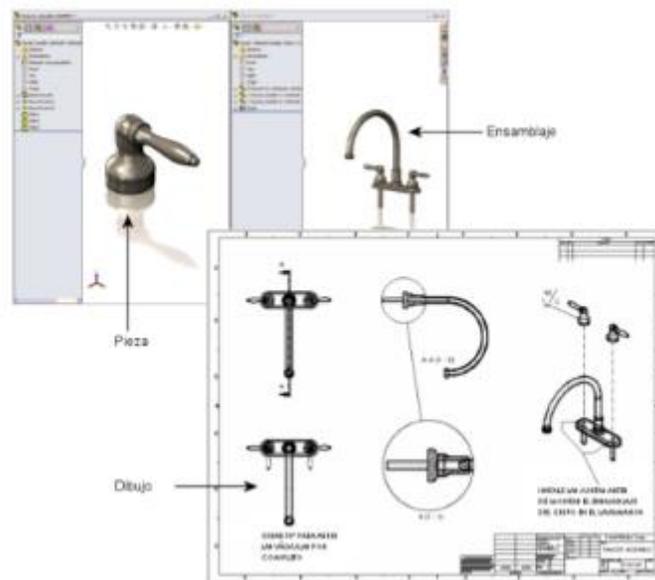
Pieza, ensamblaje y dibujo de grifería realizado en Solidworks
